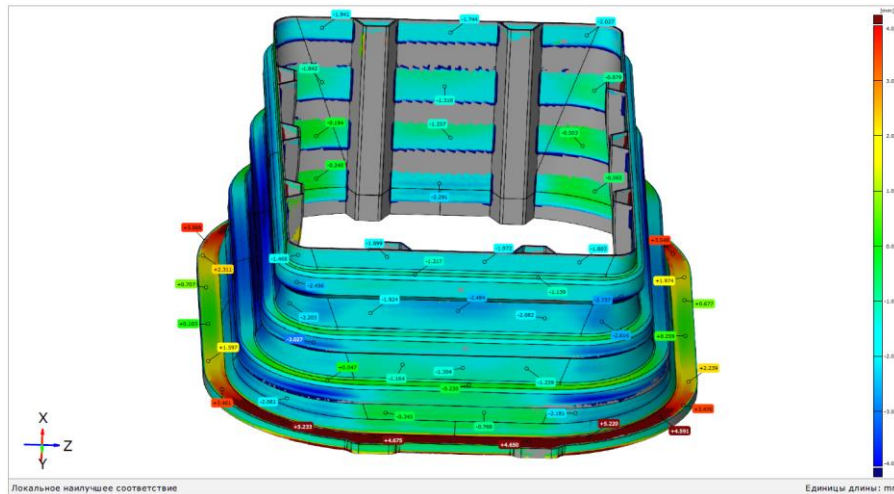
Результаты замеров заготовки детали «Корпус» на ATOS
